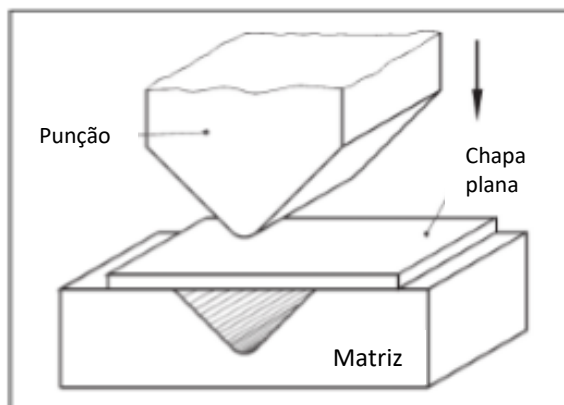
Processo de dobramento de chapa (retirada de [8])
